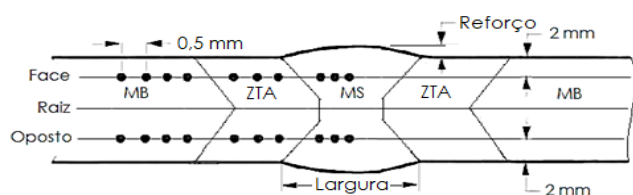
Esquema indicando os pontos de medição de dureza na junta soldada.
